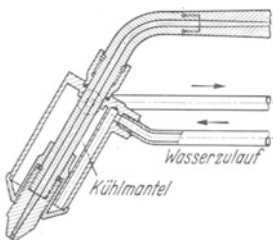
Wassergekühlter Maschinenschweißbrenner.
